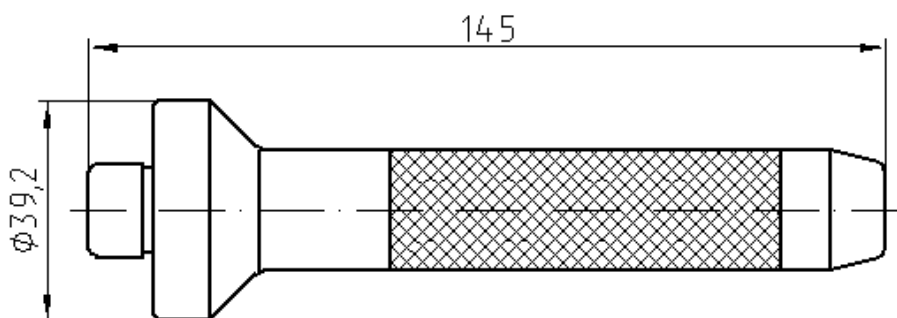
5-У-10897, Оправка для запрессовки и выпрессовки подшипника первичного вала коробки передач
